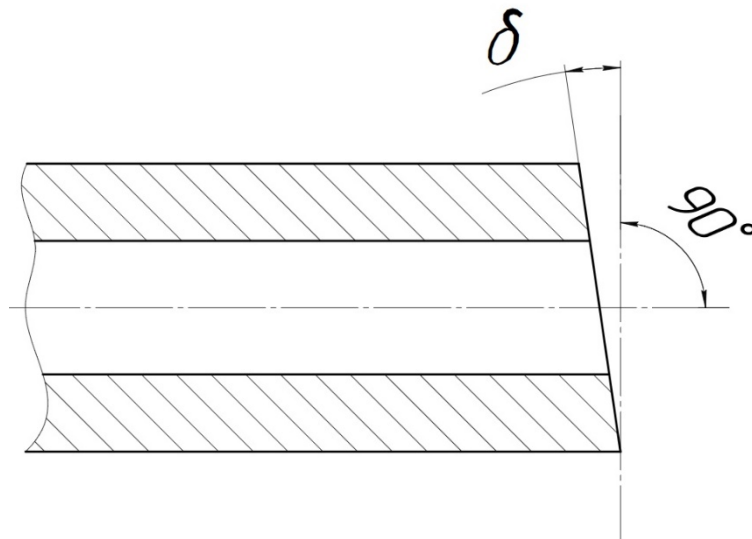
Схема расположения опорного торца обрабатываемой детали
